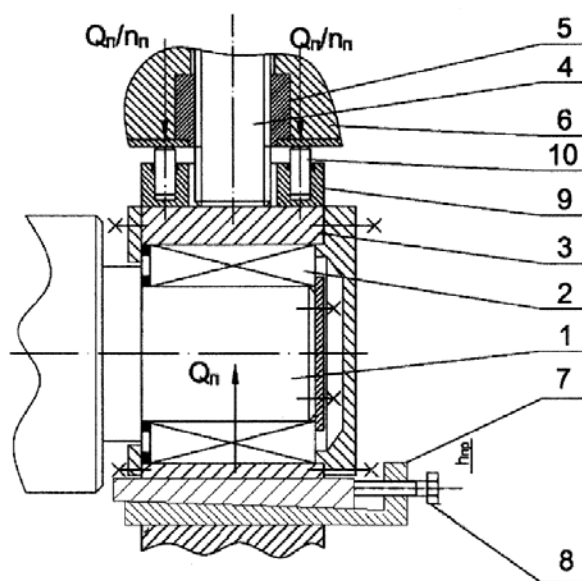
Конструкція комбінованого гідромеханічного натискного механізму чистових робочих клітей станів для гарячої прокатки сортових смугових і стрічкових заготовок
